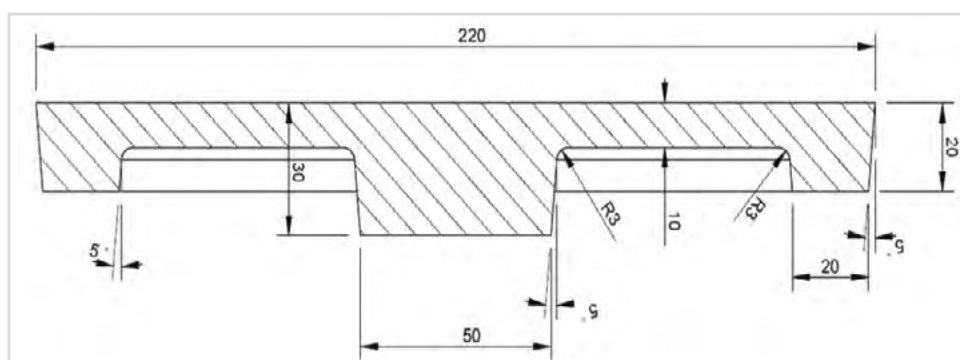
Layout eines scheibenförmigen Prototypengussteils
